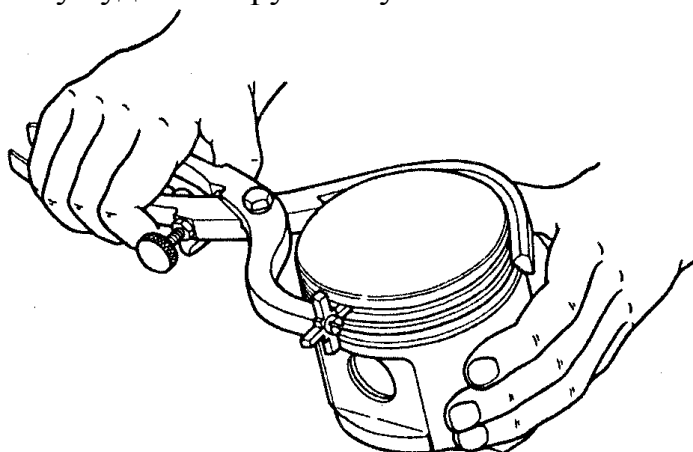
Очистка канавок поршневых колец от нагара с помощью приспособления 5-У-27691
